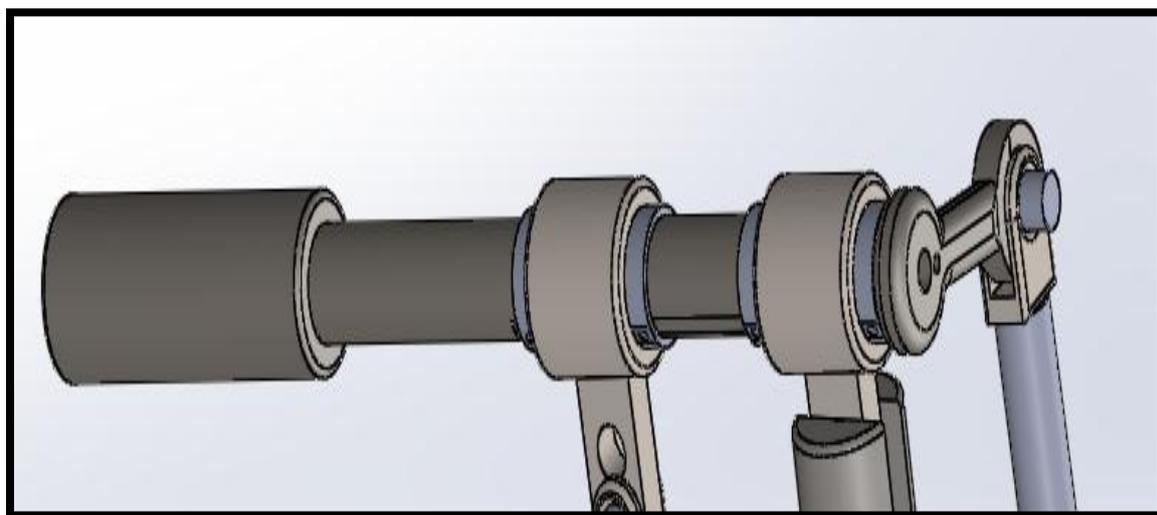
Diseño de AutoCAD 3D palanca de ejecución freno acelerador
